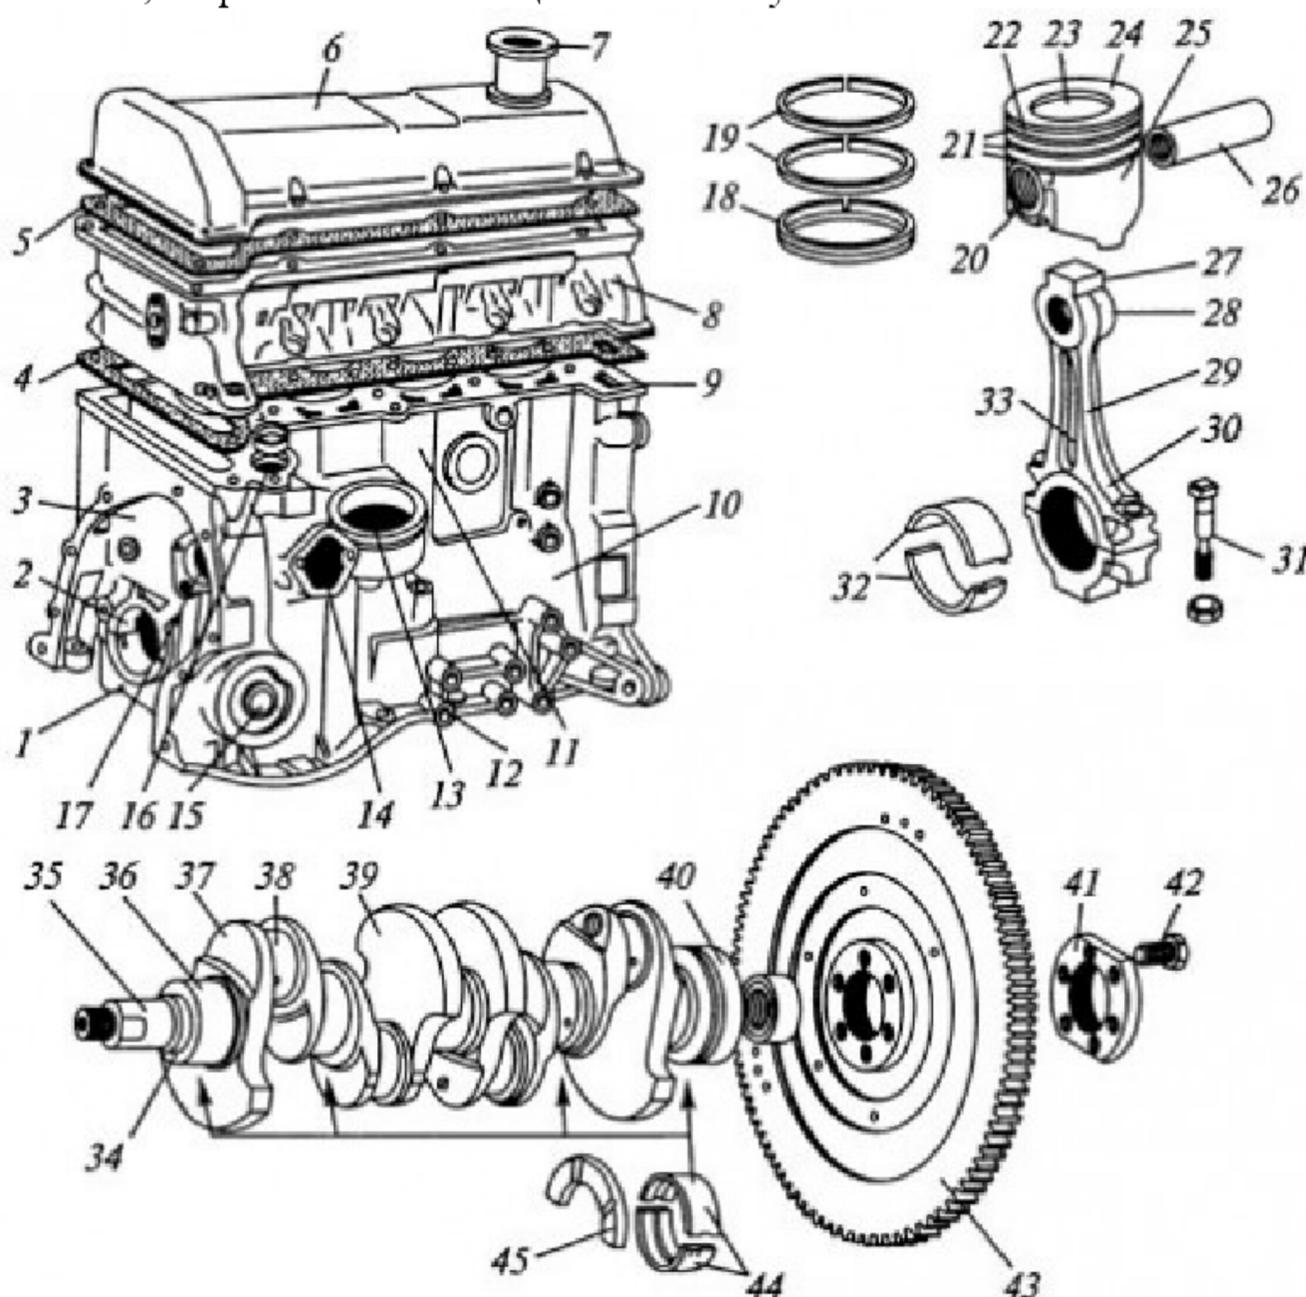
Кривошипно-шатунный механизм двигателей легковых автомобилей:
